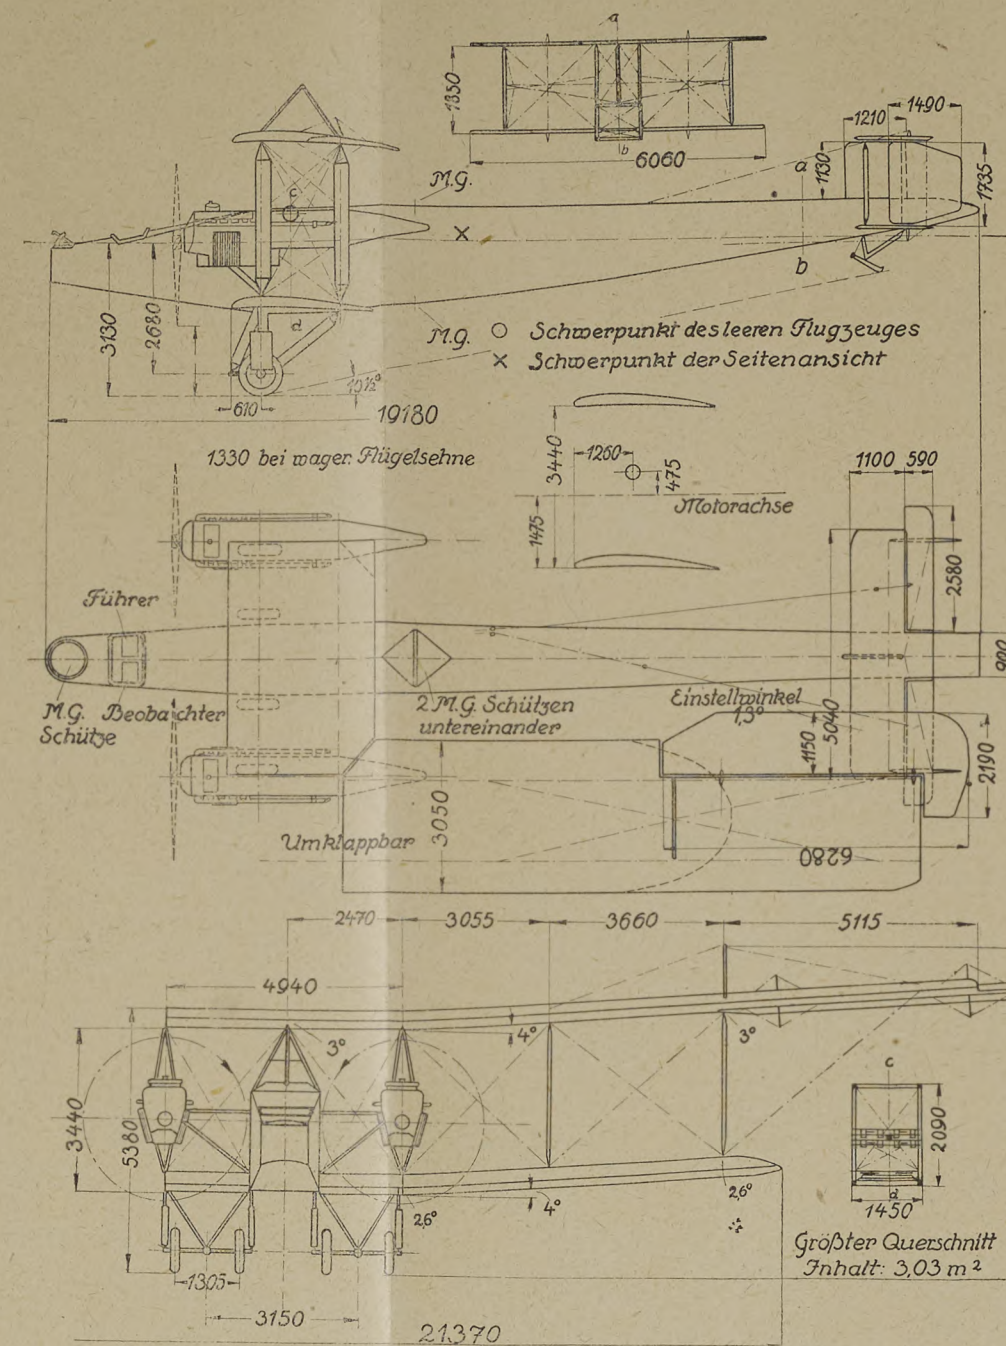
Handley-Page-G-Flugzeug. Seitenansicht, Draufsicht, Vorderansicht.
